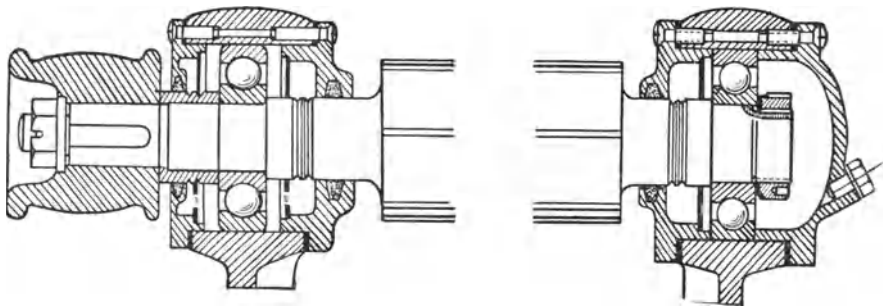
Lagerung der Messerwelle einer Hobelmaschine. Präzisions-Kugellagerwerke „Fichtel u. Sachs“ Schweinfurt.
